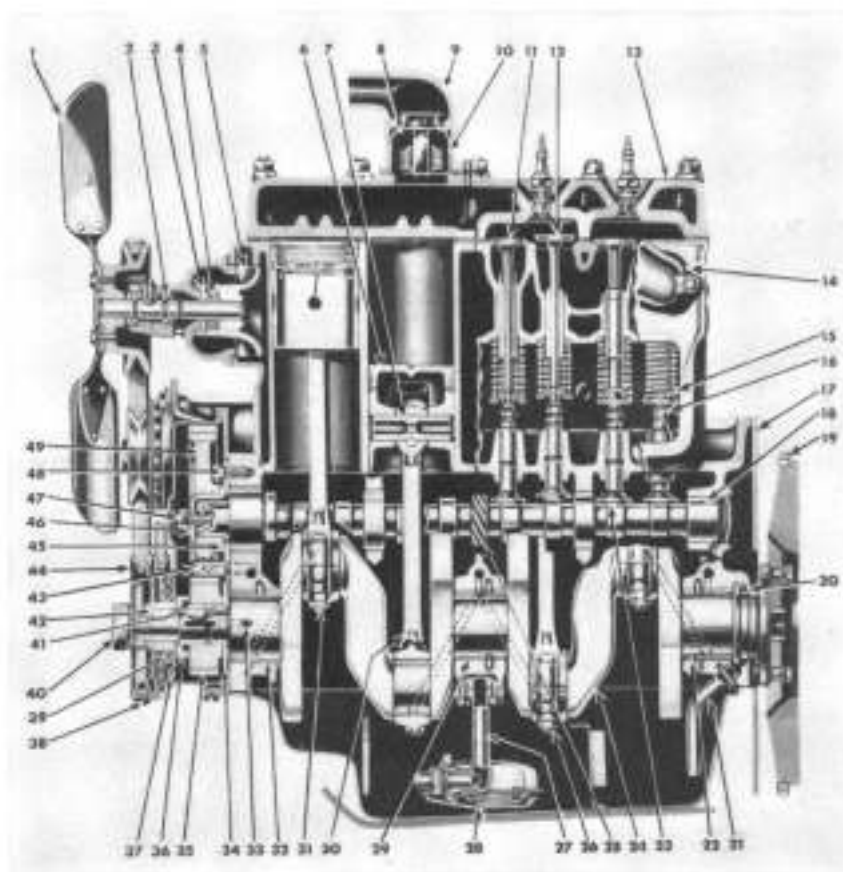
COUPE LONGITUDINALE DU MOTEUR.
